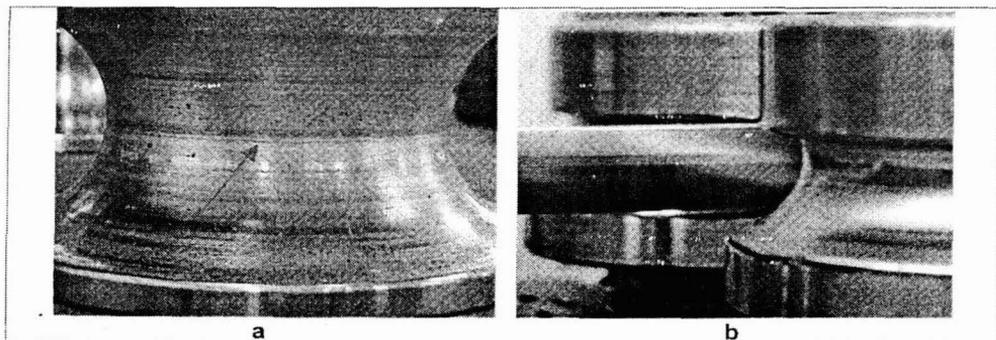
a) vista do desgaste do rolo; b) vista processo de formação do tubo
